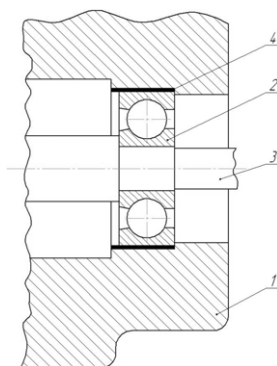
Схема посадки подшипника качения в гнездо корпусной детали: 1 – корпусная деталь; 2 – подшипник; 3 – вал; 4 – слой клеевой композиции
